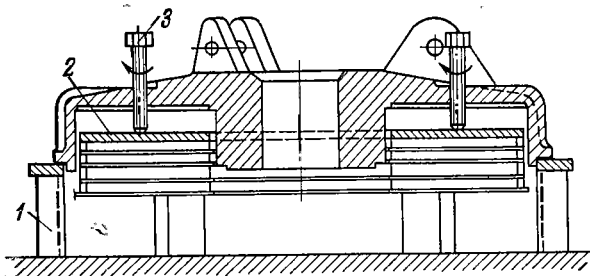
Выемка катушки из корпуса электромагнитов М-22Б, М-42Б и М-62Б.
